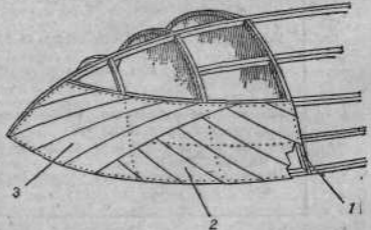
Схема обшивки бортов в носовой части лодки. 1 — шпангоут, 2 — первый слой обшивки; 3 — второй слой обшивки.
